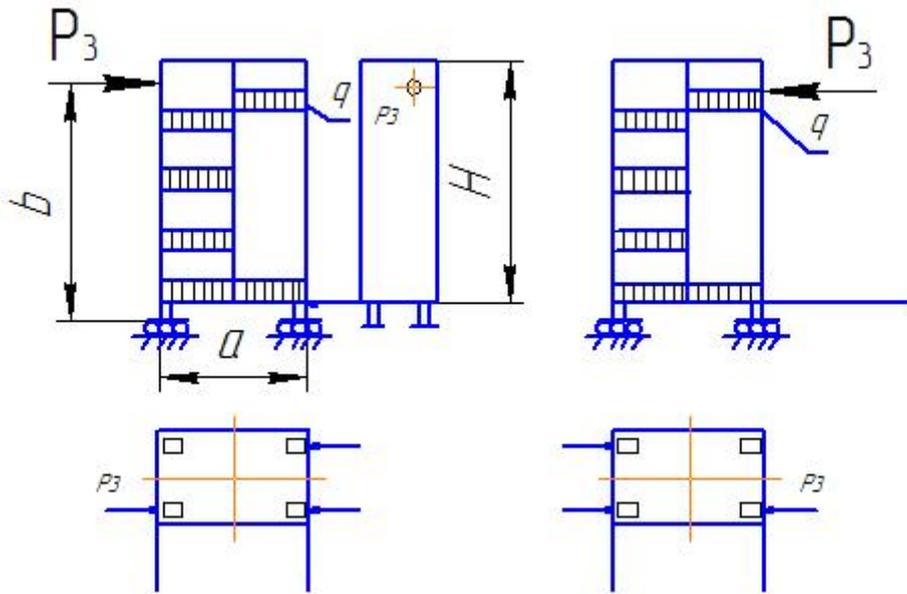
а. Схема приложения нагрузки к боковым стенкам
